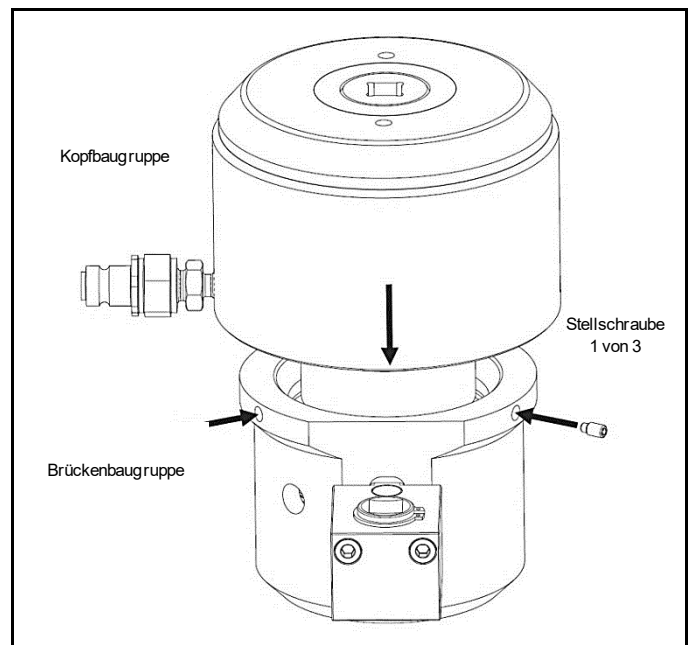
Kopfbaugruppe auf die Brückenbaugruppe setzen und mit den Gewindestiften sichern
